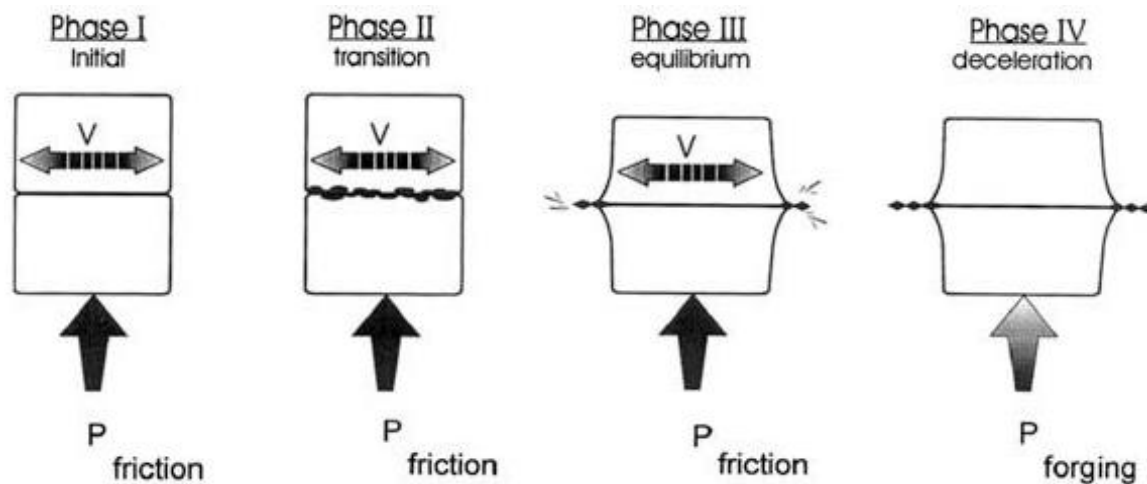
Le quattro fasi che caratterizzano la linear friction welding: iniziale, transizione, equilibrio e decelerazione [19]
